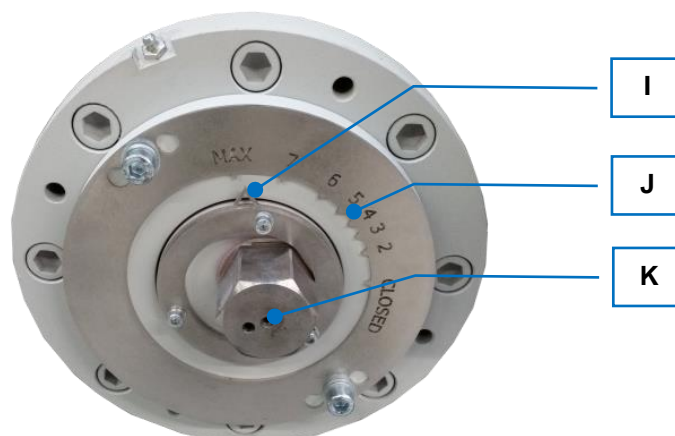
Шпиндель с винтовой резьбой – Настройка ширины зазора
